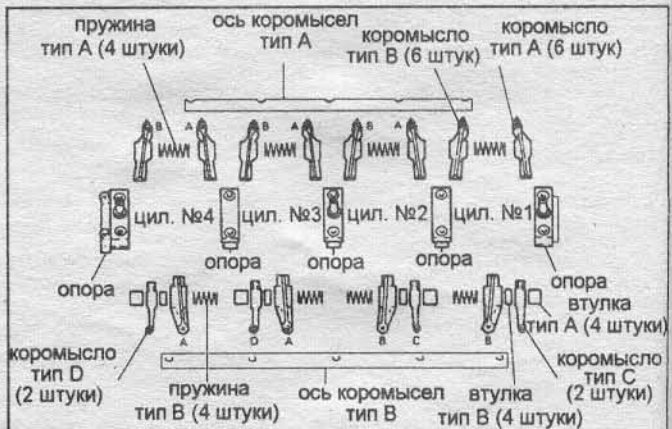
Сборка узла осей коромысел (карбюраторные двигатели).
